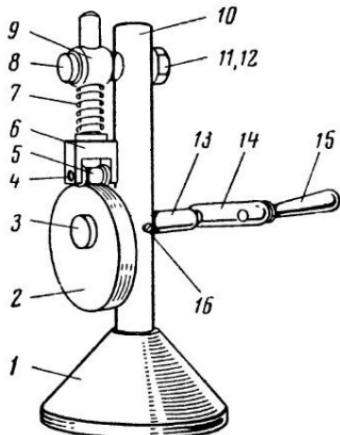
Модель кулачкового механизма: 1 — основание; 2 — кулачок; 3 — вал привода; 4 — ось ролика; 5 — ролик; 6 — шток; 7 — направляющая пружина; 8 — направляющий винт; 9 — кронштейн; 10 — стойка; 11 — шайба; 12 — гайка; 13 — упорная втулка; 14 — рычаг привода; 15 — ручка; 16 — стопорный винт.
